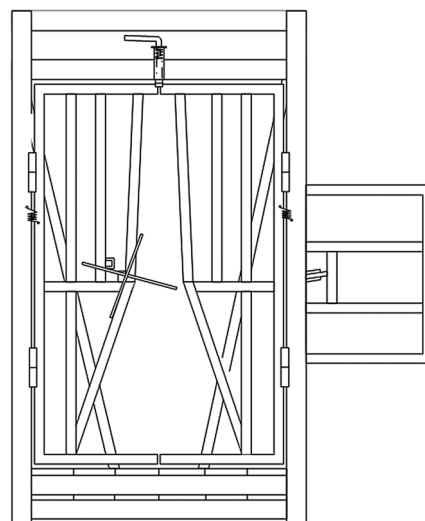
Поворотный станок для искусственного осеменения овец, вид спереди
